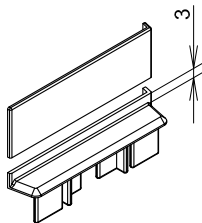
Bearbeitung der Endkappe 9C24 unten. Zuschnitt wie oben (Abb.4) und zusätzliches Entfernen des Überstandes.
